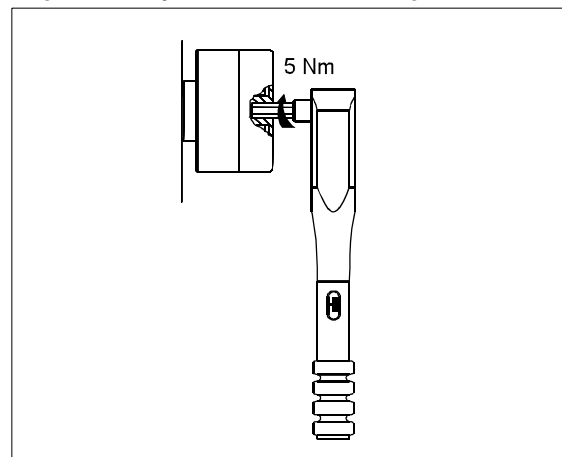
Tampa da carcaça com chave dinamométrica apertar
